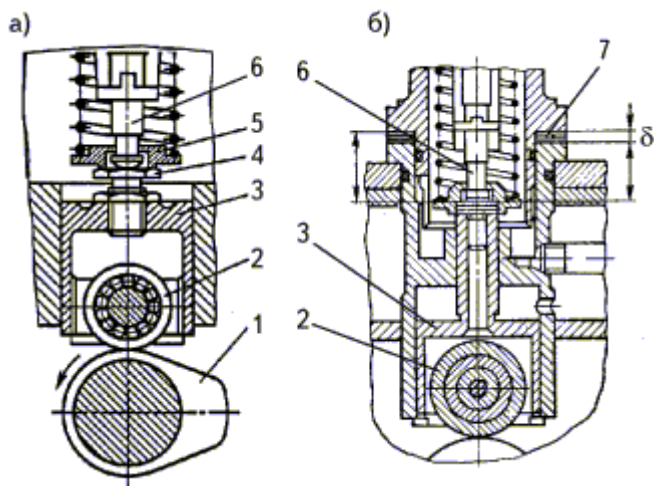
Фрагмент конструкции топливного насоса: а – с резьбовой регулировкой (дизель 11Д45); б – с регулировкой прокладками (Д70); 1 – кулачок; 2 – ролик толкателя; 3 – толкатель; 4 – регулировочный винт; 5 – тарелка пружины; 6 – хвостовик плунжера; 7 – регулировочные прокладки
